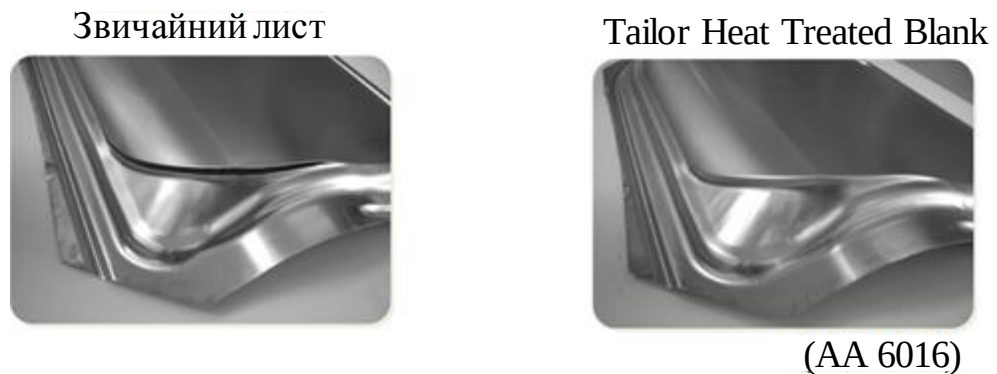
Елемент кузова автомобіля після штамповки, виготовлений зі звичайного листа з алюмінієвого сплаву AA6016 та Tailor Heat Treated Blank [3]
